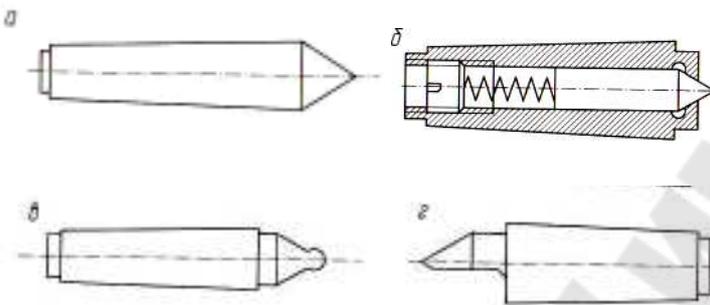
Схемы неподвижного (жесткого) (а), плавающего (б), сферического (в) центров и полуцентра (г)
